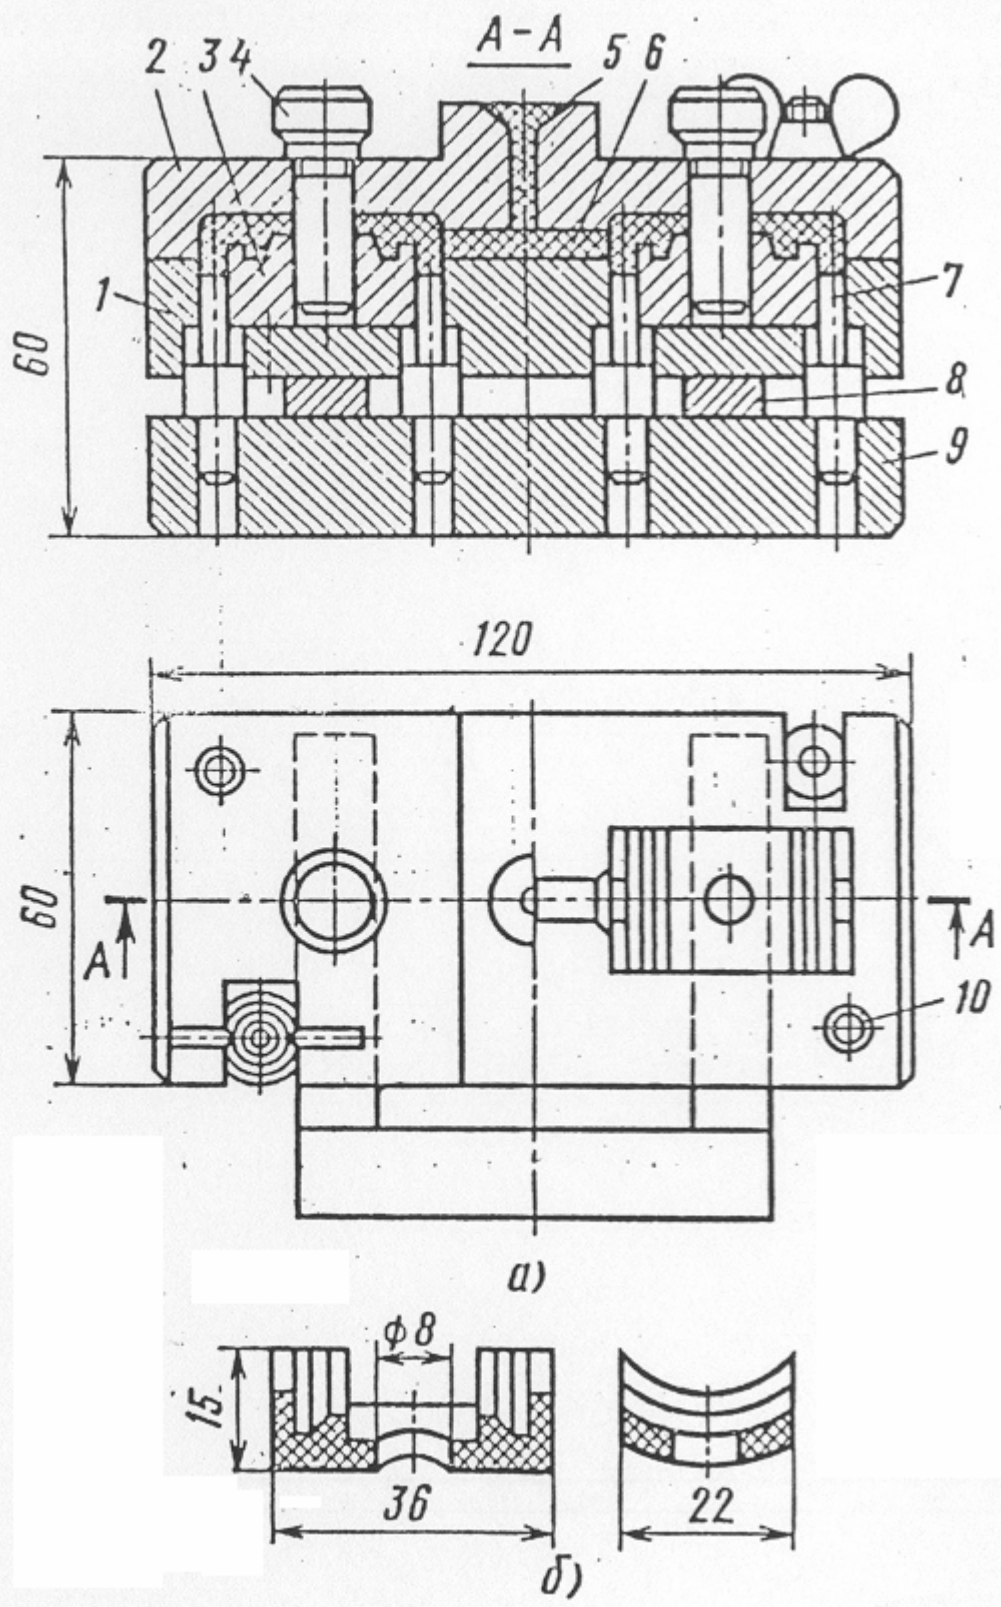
Пресс-форма для изготовления моделей в серийном производстве (а) и модель (б): 1 – нижняя матрица; 2 – верхняя, съемная матрица; 3 – вставки; 4 – подвижный стержень; 5 – литниковый канал; 6 – питатели; 7 – толкатели; 8 – фиксатор; 9 – плита основания; 10 – направляющие штыри.
